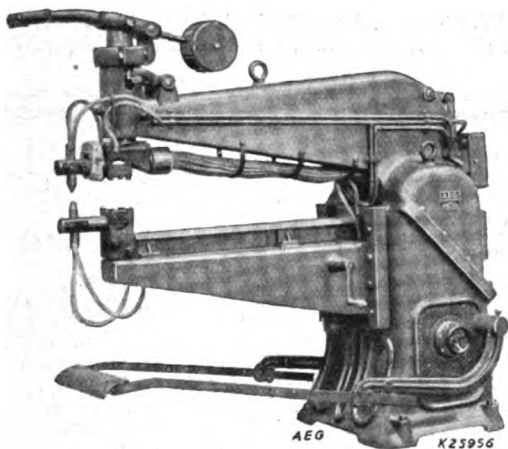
Punktschweißmaschine mit 1,2 m Armausladung.
